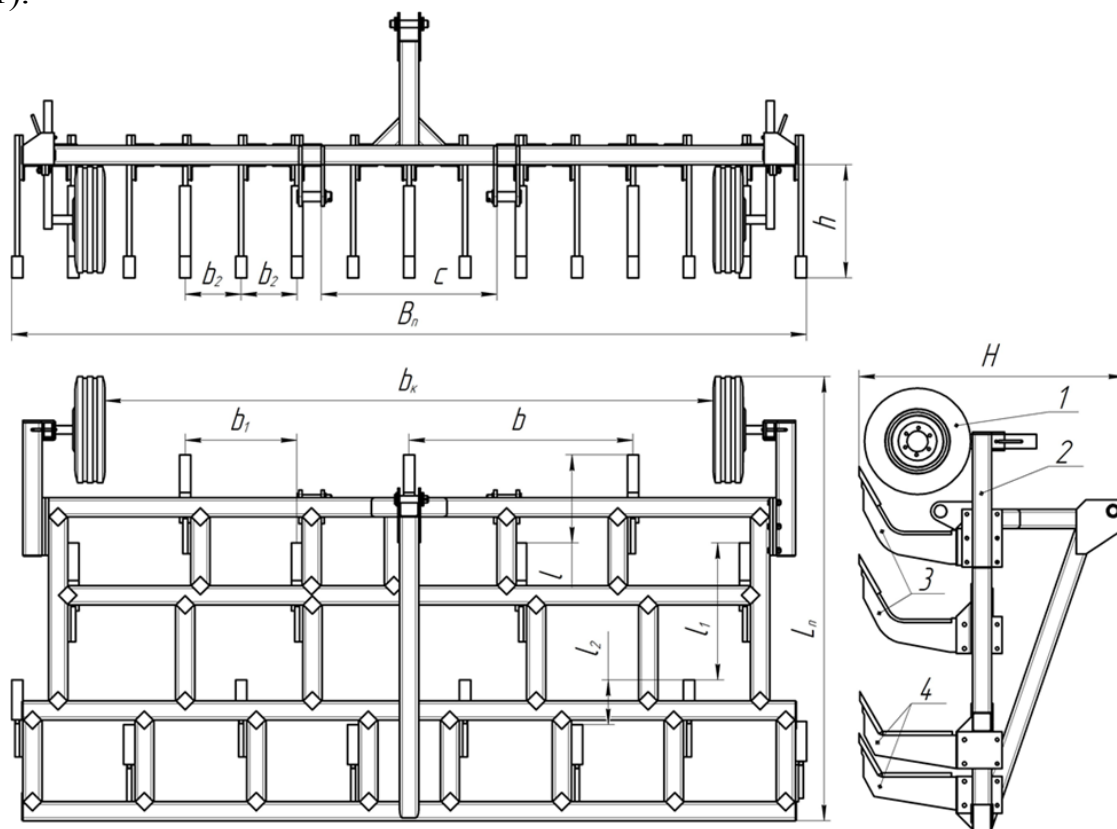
Конструктивно-технологическая схема навесного фронтального плуга-рыхлителя для агрегатирования с тракторами тягового класса 5: 1 – опорное колесо с механизмом регулировки глубины обработки; 2 – рама с навесным устройством; 3 – чизельные рабочие органы с грудкой; 4 – чизельные рабочие органы; B_n – ширина захвата плуга (4,970 м); H – высота плуга (1,658 м); L_n – длина плуга (2,777 м); b_k – расстояние между опорными колесами (3,805 м); b – расстояние между рабочими органами в первом ряду (1,40 м); b_d – ширина долота чизельного рабочего органа (0,07 м); b_1 – расстояние между смежными рабочими органами в ряду (0,7 м); b_2 – расстояние между рабочими органами (0,35 м); l – расстояние между рабочими органами первого и второго ряда (0,55 м); l – длина долота чизельного рабочего органа (0,31 м) l_1 – расстояние между рабочими органами второго и третьего ряда (0,857 м); l_2 – расстояние между рабочими органами третьего и четвертого ряда (0,280 м); α – угол постановки долота ко дну обрабатываемого слоя почвы (27 град.).
